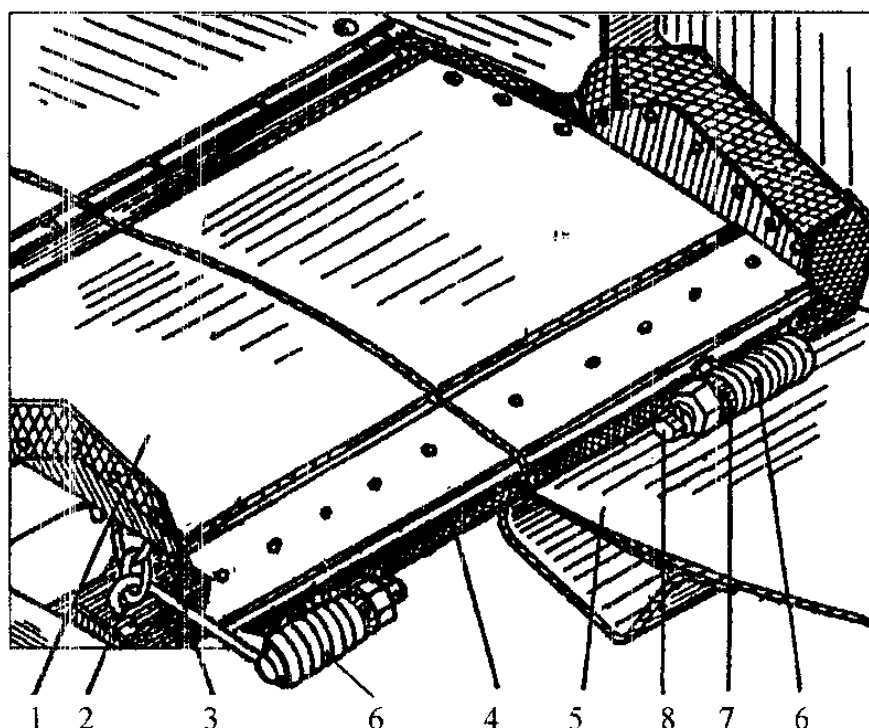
Переходной уплотнительный щит*: 1 – щит; 2 – соединительное звено; 3, 4 – прорезиненные ремни; 5 – днище проставки; 6 – пружина; 7 – зацеп с рифлениями; 8 – болт
